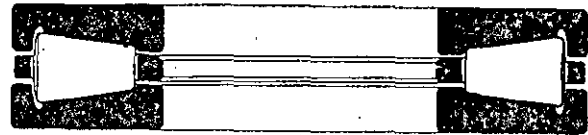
Rodamiento de rodillos cónicos de empuje axial. Este rodamiento puede soportar fuertes cargas axiales.
